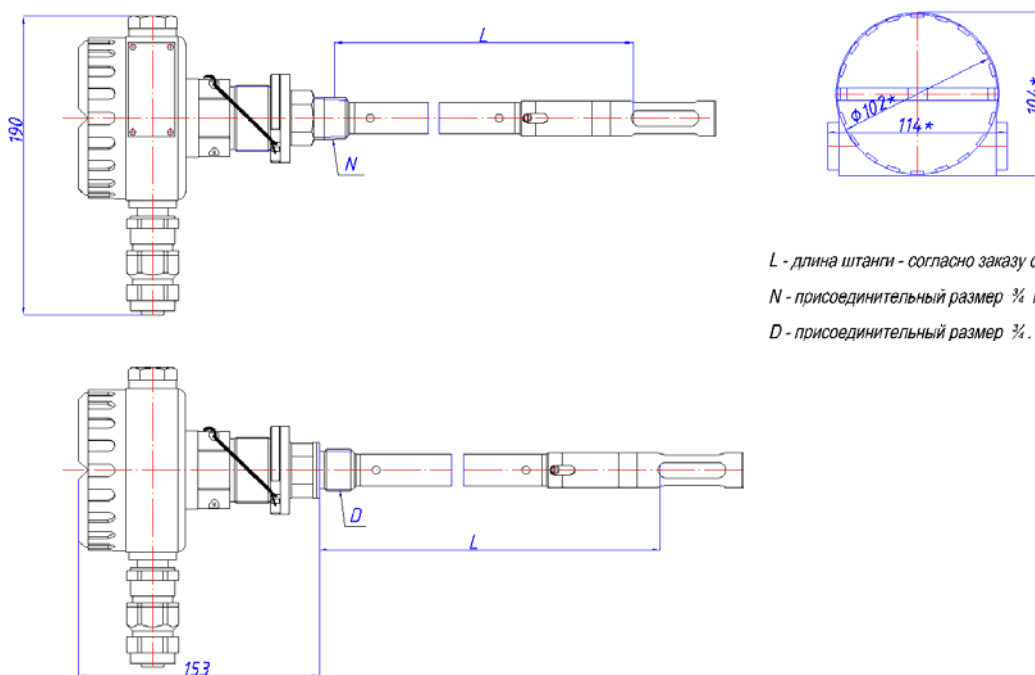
Внешний вид, габаритные и установочные размеры
